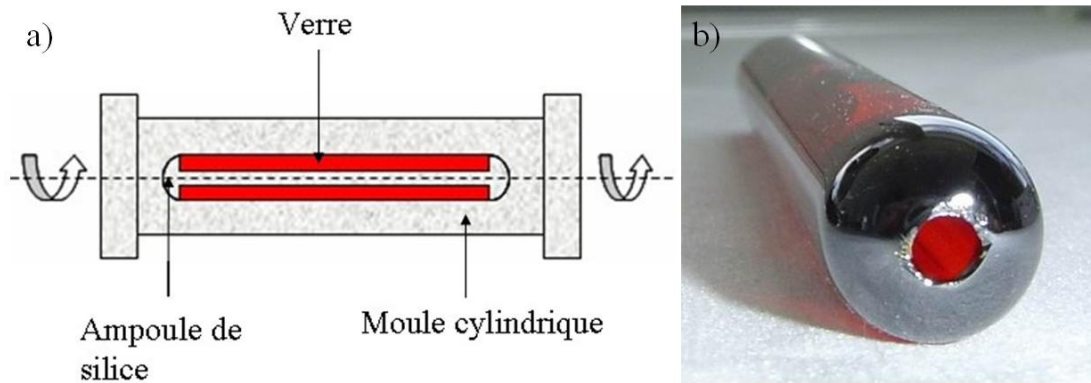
a) Principe du rotational casting. b) Tube de verre au soufre
